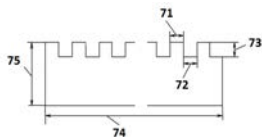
Представлена развертка бортика датчика с геометрическими размерами выступов и углублений на гребне (на кромке) бортика.
